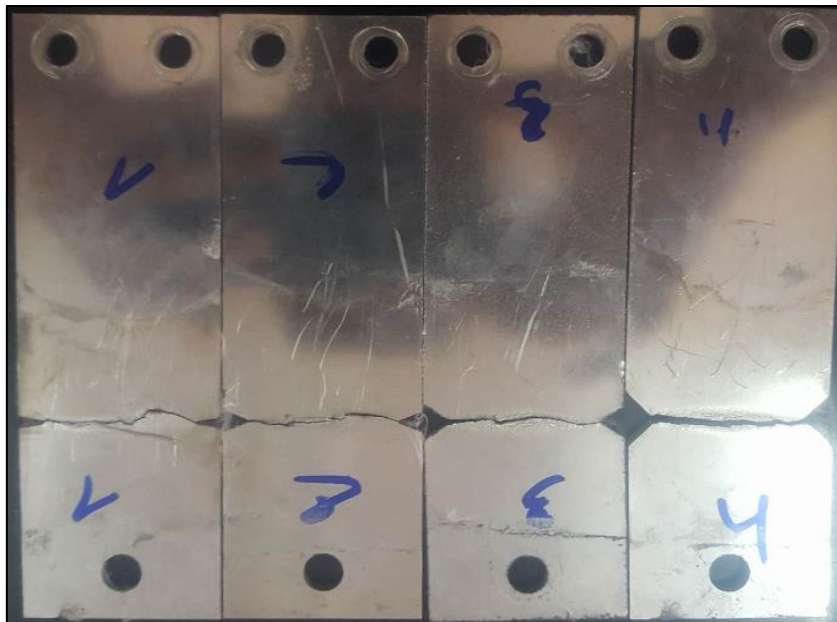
Eprouvettes aux entailles en « V » après la rupture en fatigue sous corrosion.
